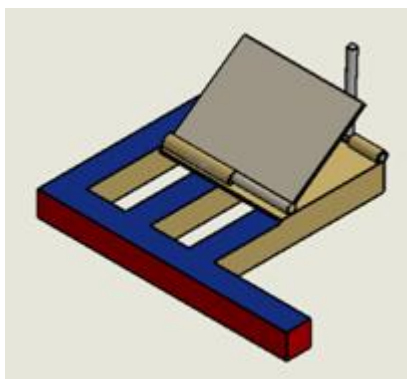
2 Diseño de la Base para Motor Trifásico
